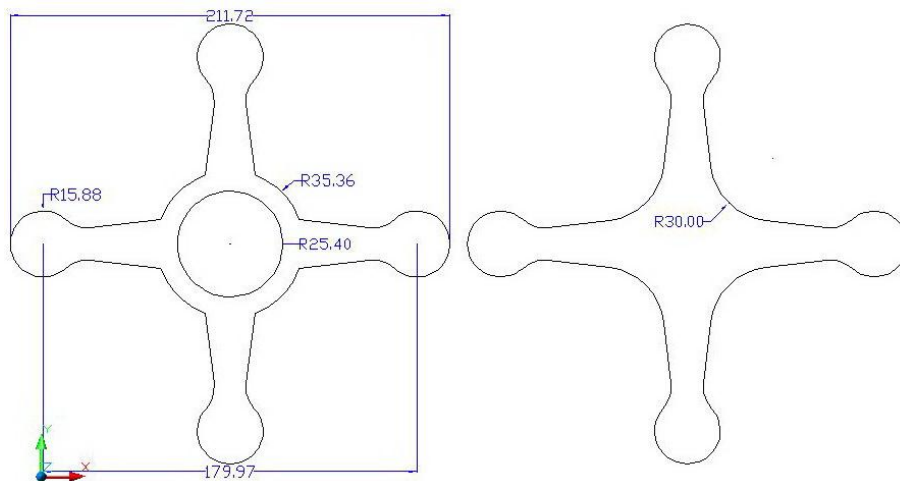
Gambar dasar *Planetary Gear Unit*.
